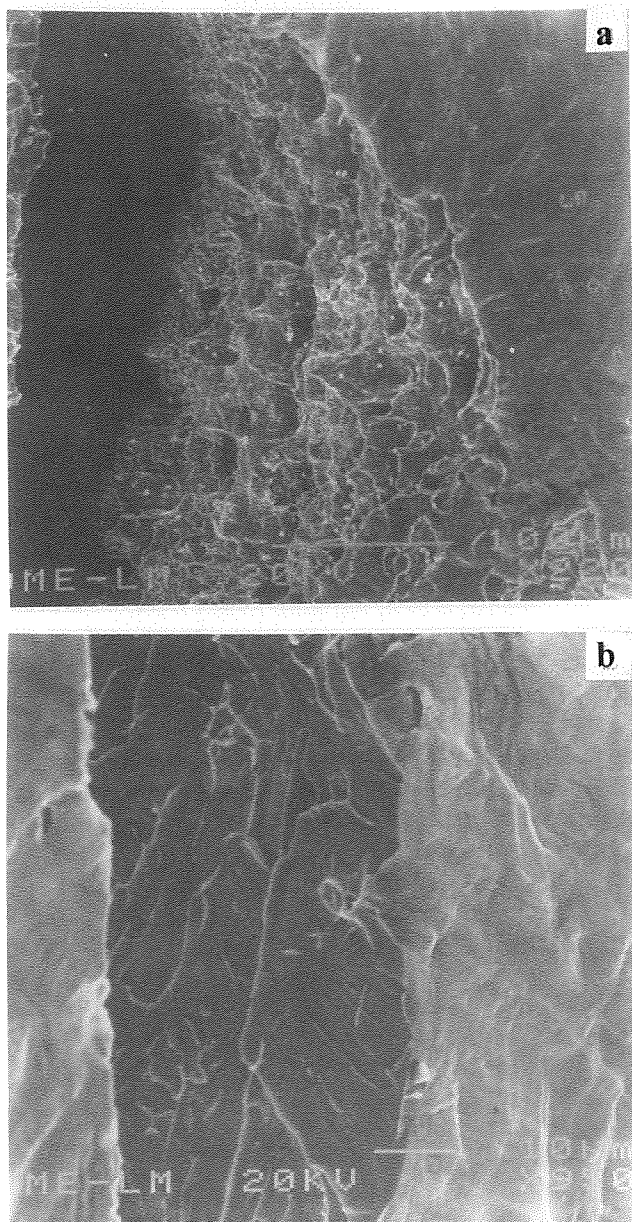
Detalle del carácter fractográfico de las grietas observadas en la Figura 5: a) dúctil para el material 275/6000 y b) frágil para el material 475/25.
